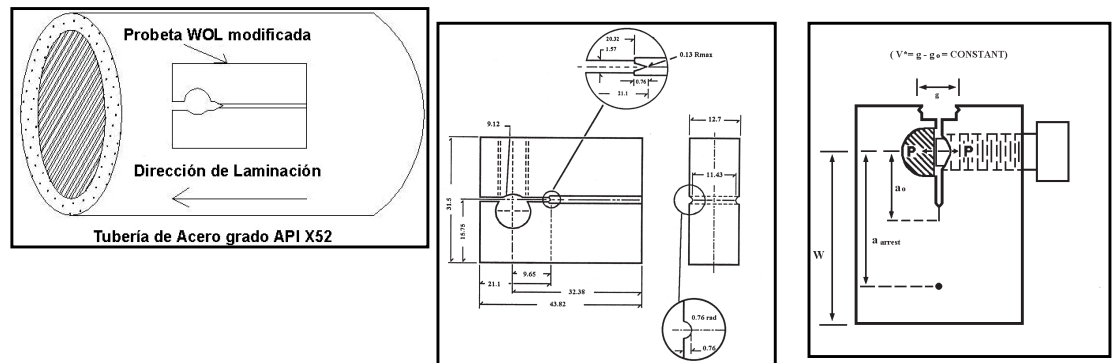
Probeta MWOL modificada, dimensiones y dirección de corte-maquinado.
